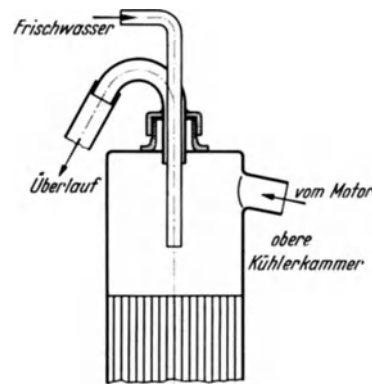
Führungsstück für Kühlwasserzu- und -ablauf.
